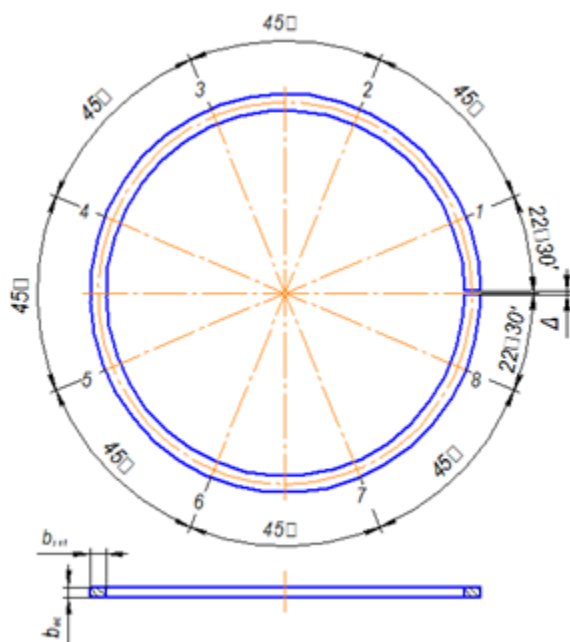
Схема микрометрирования размеров полноразмерного поршневого компрессионного кольца двигателя 6Ч12/14СП (К-551)
